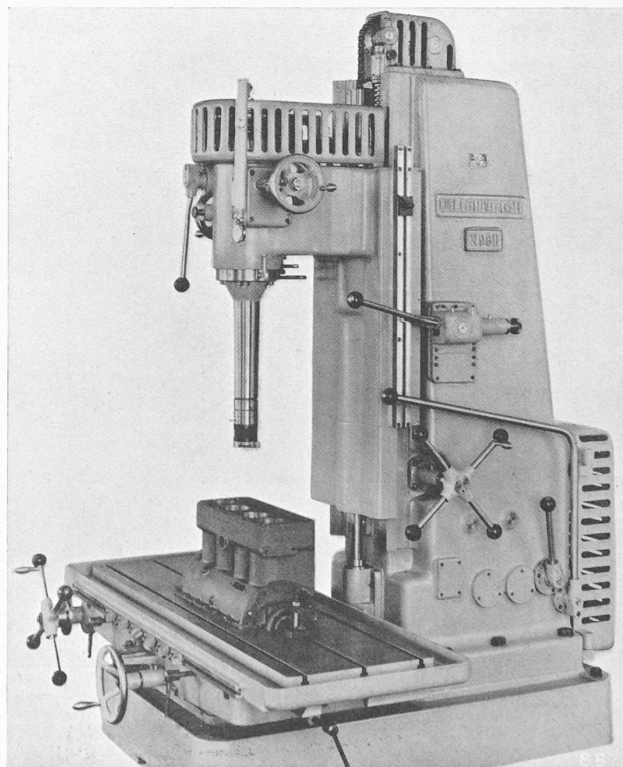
Feinbohrwerk der Kellenberger Werkzeugmaschinenfabrik, St. Gallen.
